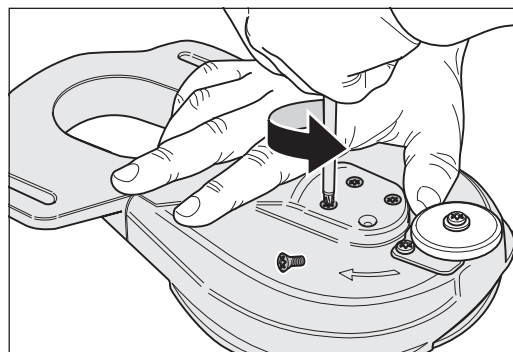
Die vier Befestigungsschrauben des kompletten Schleiftellers entfernen.
